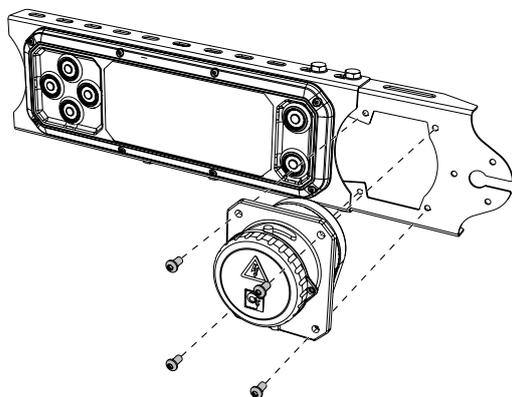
Montaje del interruptor principal junto al dispositivo de mando CD 19
